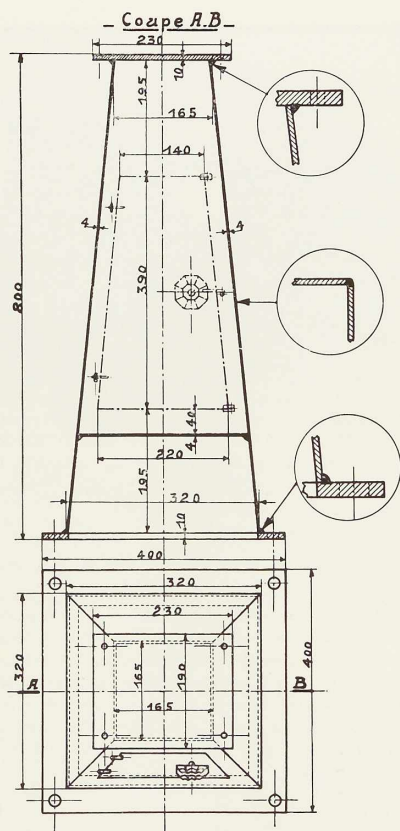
Plan de construction d'un bâti de meule soudé (voir fig. 669).
